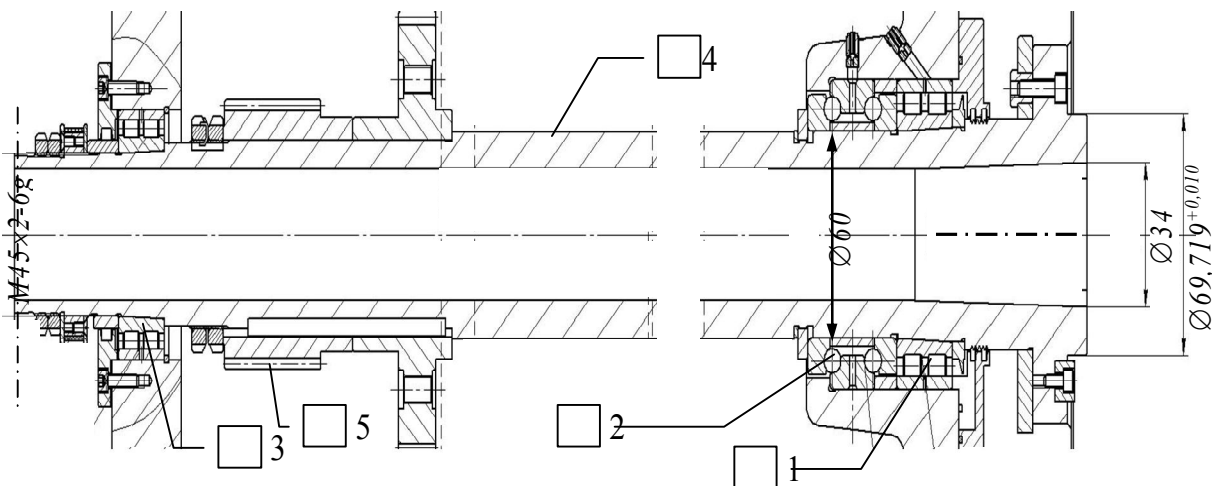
Шпиндель верстата на підшипниках кочення; позиціями показані джерела вібрацій шпинделя
